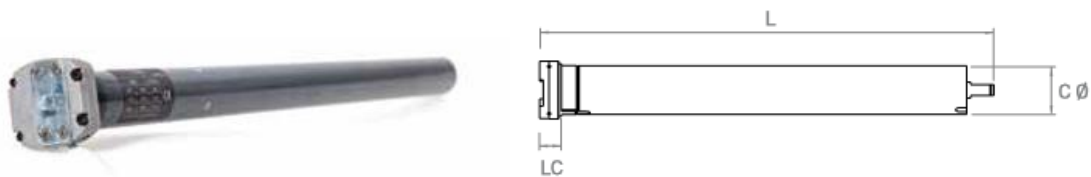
Imagen de motor mecánico y dimensiones. (Fuente: Persax)
